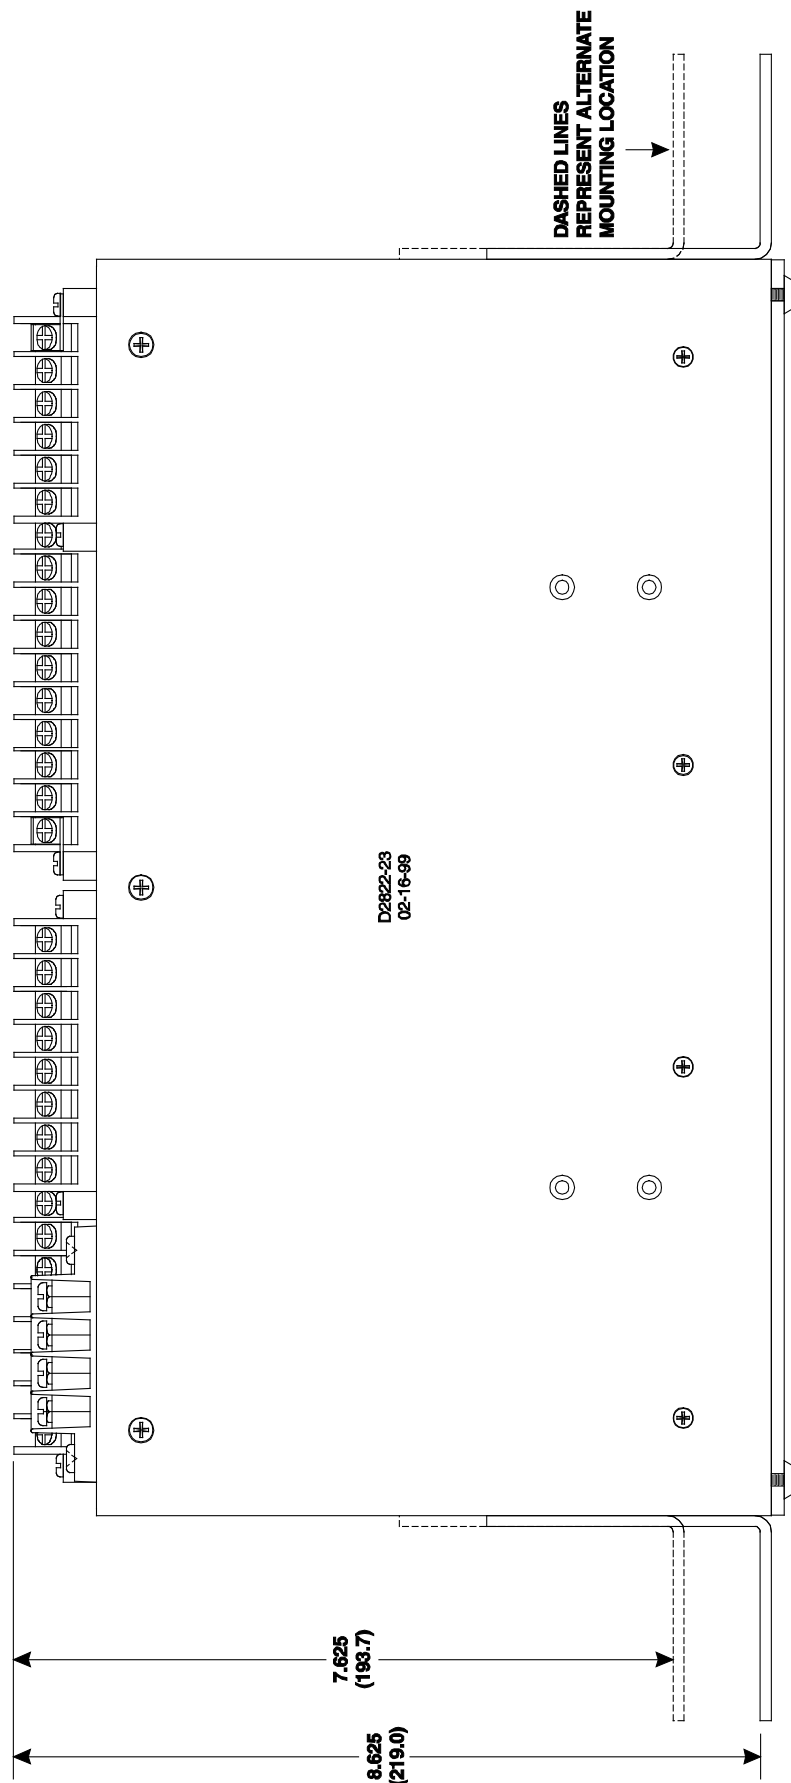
Dimensions du stabilisateur PSS-100 pour un montage en tiroir encastré, Vue de haut
